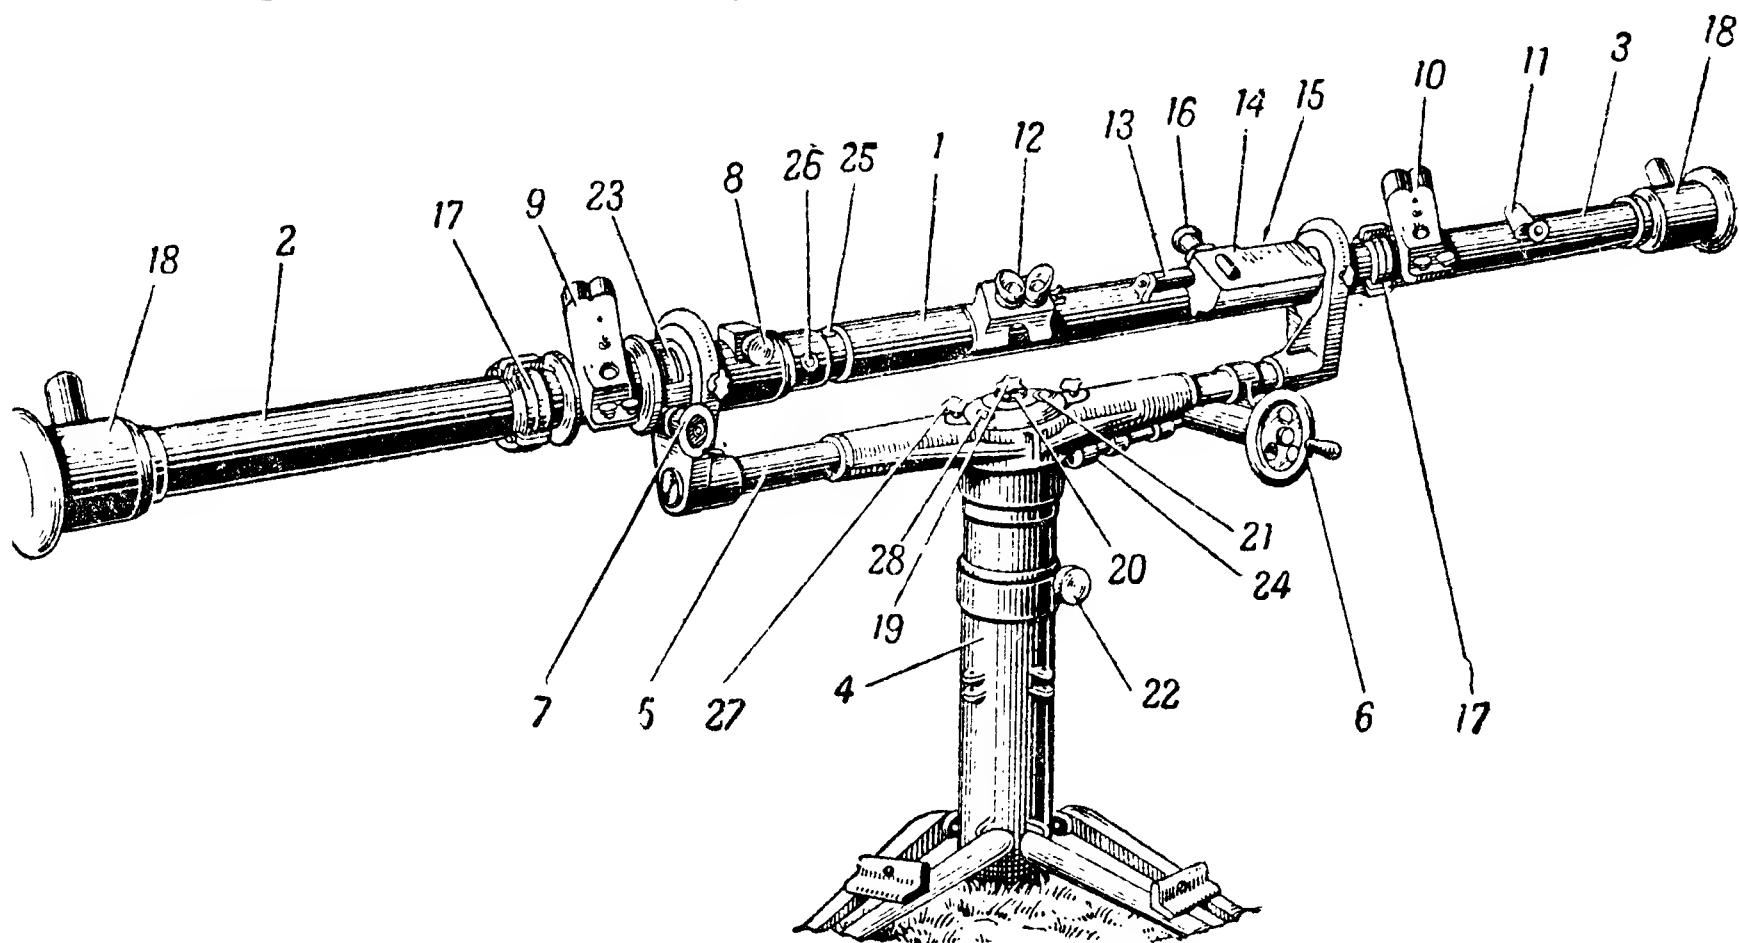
Четырехметровый стереодальномер. Расположение механизмов на наружном корпусе.
